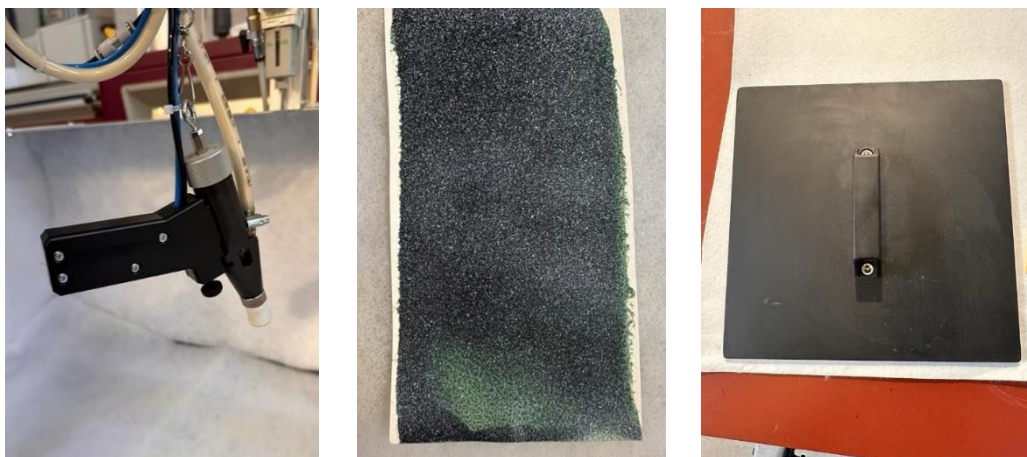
Pistola de aplicación de adhesivos en dispersión acuosa (izq), film de PU con adhesivo aplicado (centro) y plancha metálica
